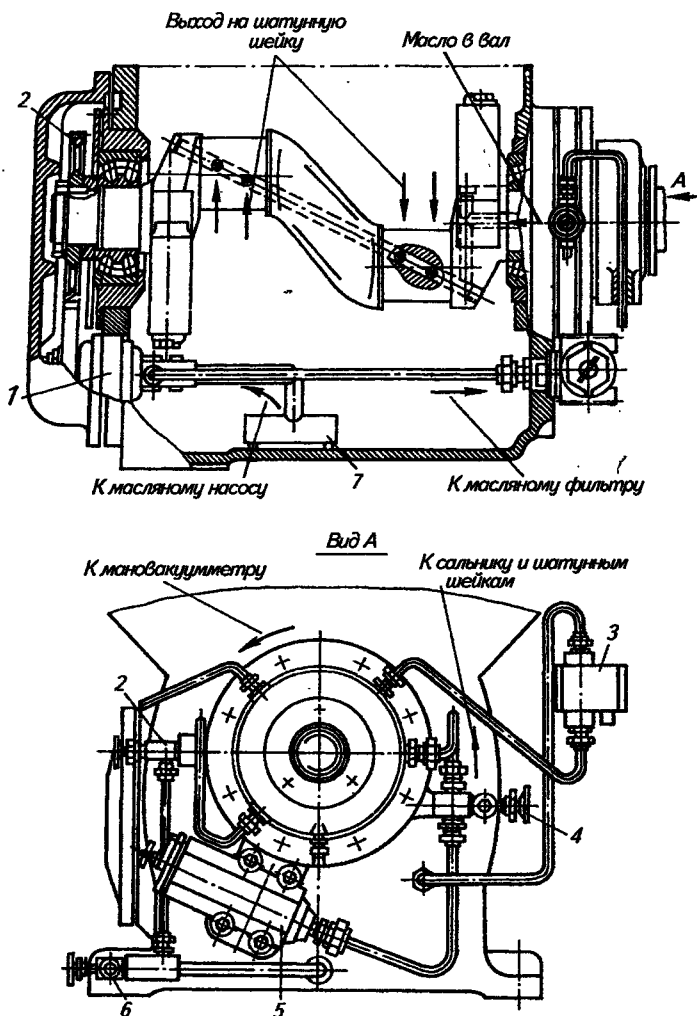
Схема принудительной циркуляционной смазки бескрейцкопфного компрессора
